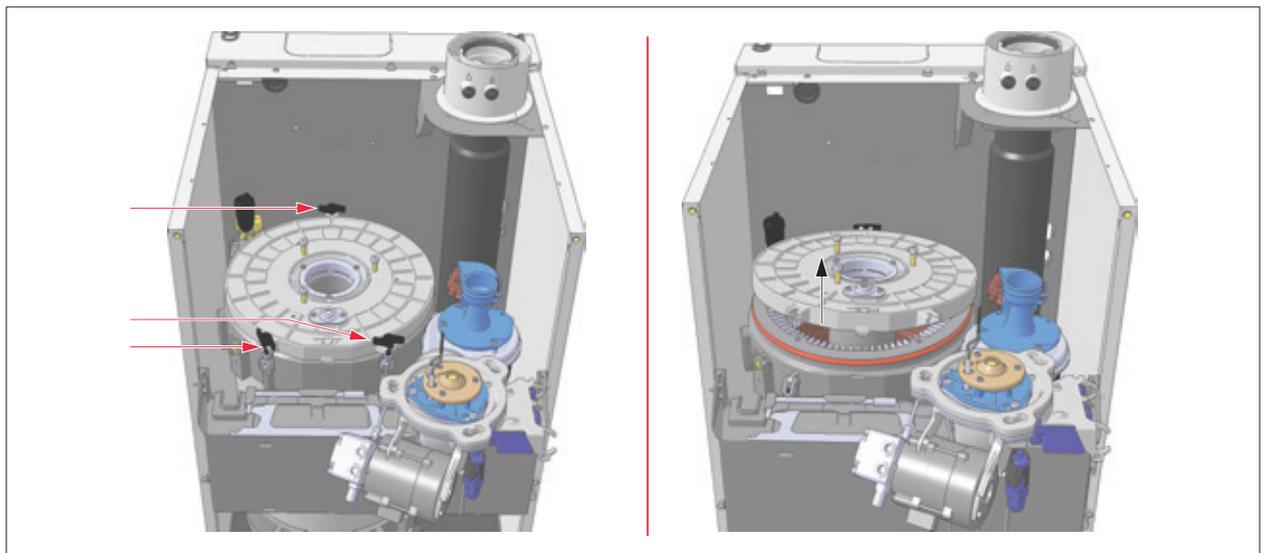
Détacher et retirer le couvercle de la chambre de combustion.
